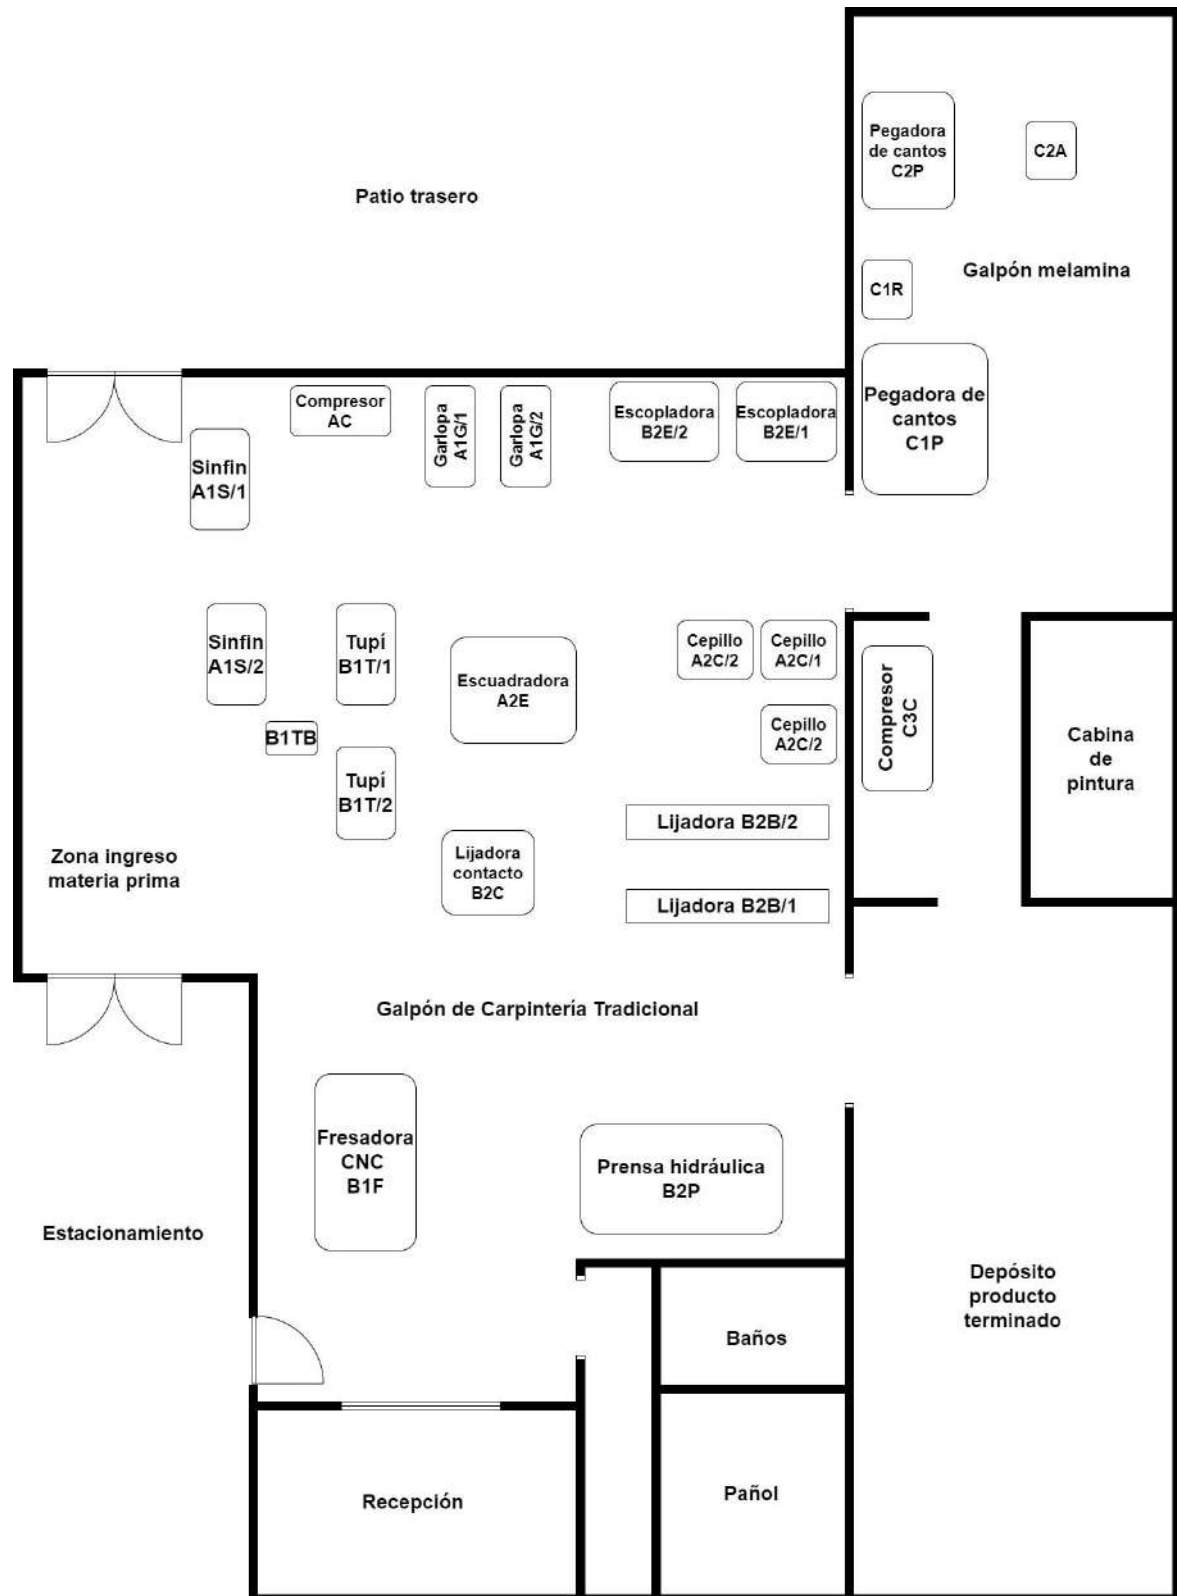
Esquema de planta con la ubicación de los equipos.
